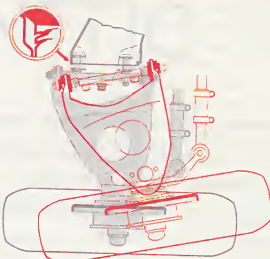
При разрушении поперечной балки в этом месте нижний рычаг вместе с колесом отклоняется в сторону.
